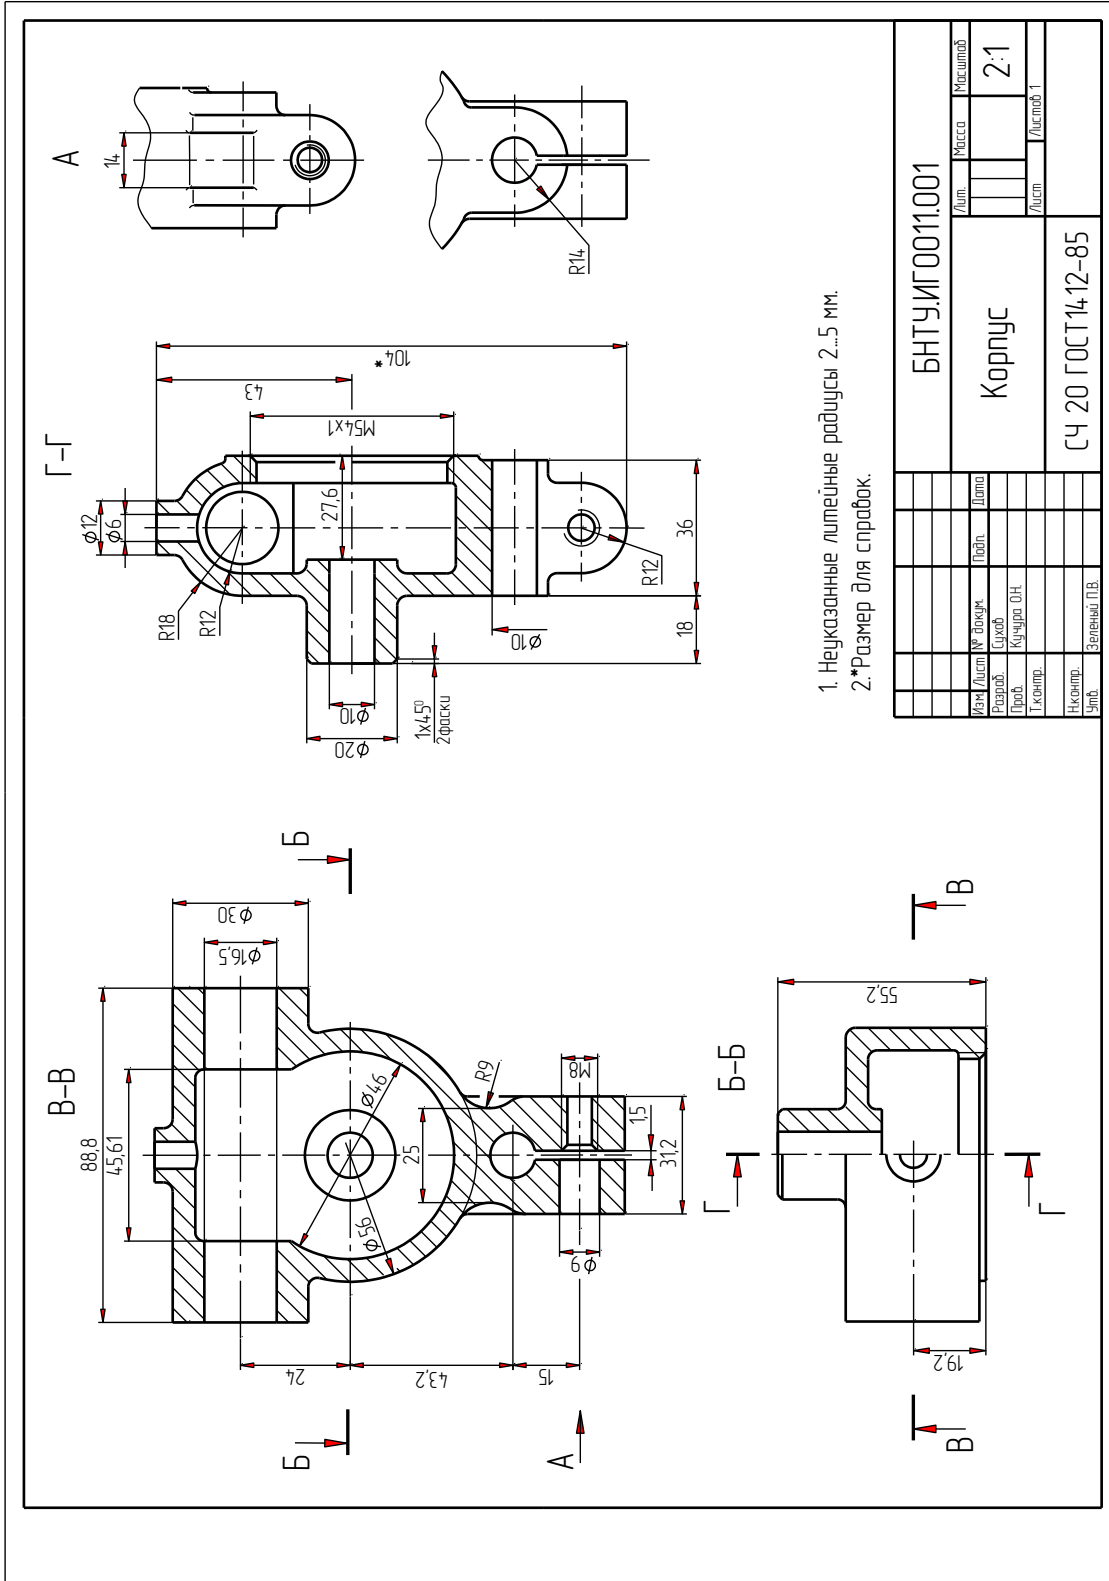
Чертеж корпусной детали, представленный основными видами и разрезами на них (вид А не находится в проекционной связи)
